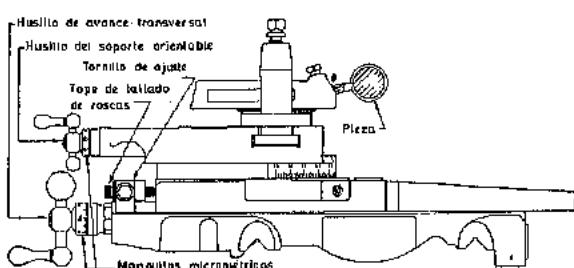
Aplicación del tope de paro ajustable para evitar que la herramienta penetre demasiado en la pieza que se roscá (South Bend Lathe Works).
